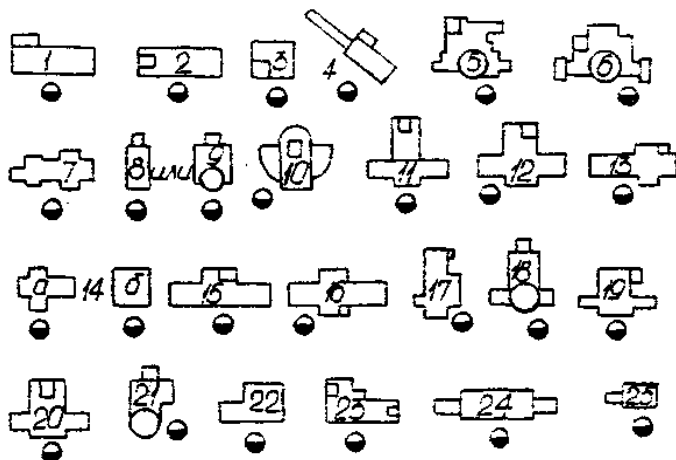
Условные графические обозначения металлообрабатывающих станков: 1 и 2 – токарно-винторезные с разным расположением электромоторов; 3 – токарный многорезцовый; 4 – револьверный автомат при прутковой работе, расположенный под углом; 5 – карусельный малый; 6 – карусельный большой; 7 – расточной; 8 и 9 – вертикально-сверлильный; 10 – радиально-сверлильный; 11 – горизонтально- и вертикально-фрезерные; 12 – универсально-фрезерный; 13 – продольно-фрезерный; 14 – зубофрезерный (а), зубострогальный и зубодолбежный (б); 15 – продольно-строгальный одноколонный; 16 – продольно-строгальный двухколонный; 17 – шепинг; 18 – долбежный; 19 – круглошлифовальный; 20 – плоскошлифовальный продольного типа; 21 – плоскошлифовальный карусельного типа; 22 – внутришлифовальный; 23 – бесцентровошлифовальный; 24 – центровальный; 25 – болторезный
